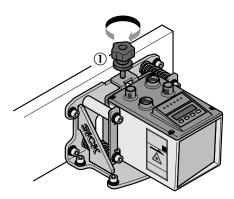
Entfernungs-Messgerät mit Rändelschraube befestigen
